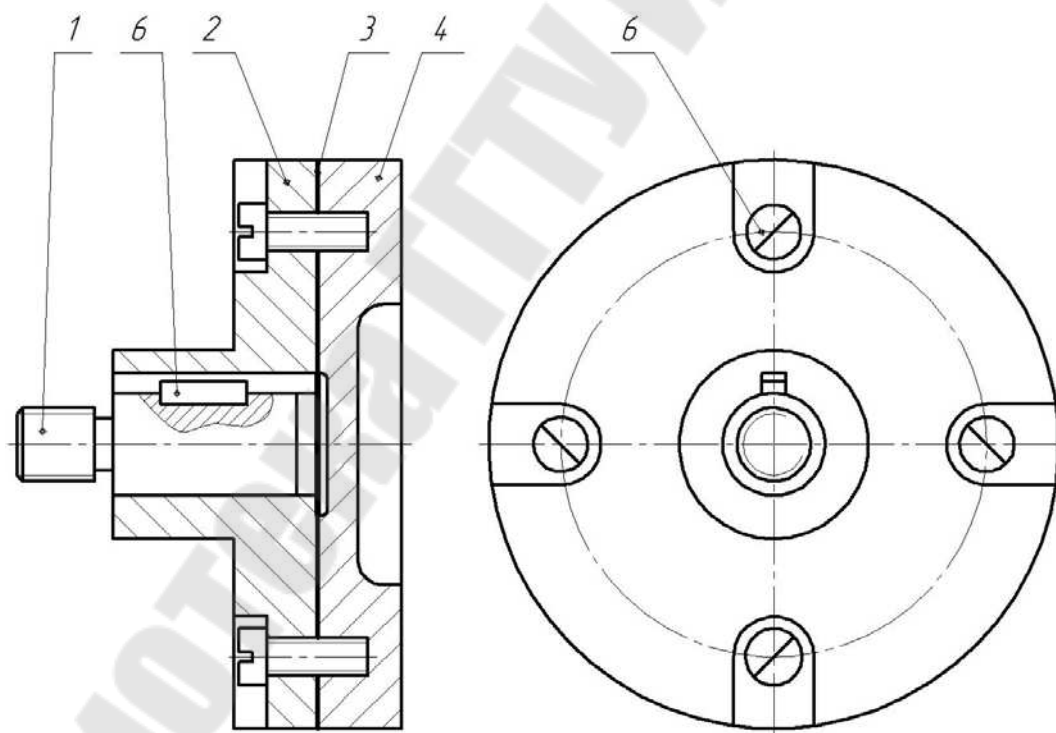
Чертеж общего вида изделия (сборочный чертеж)
